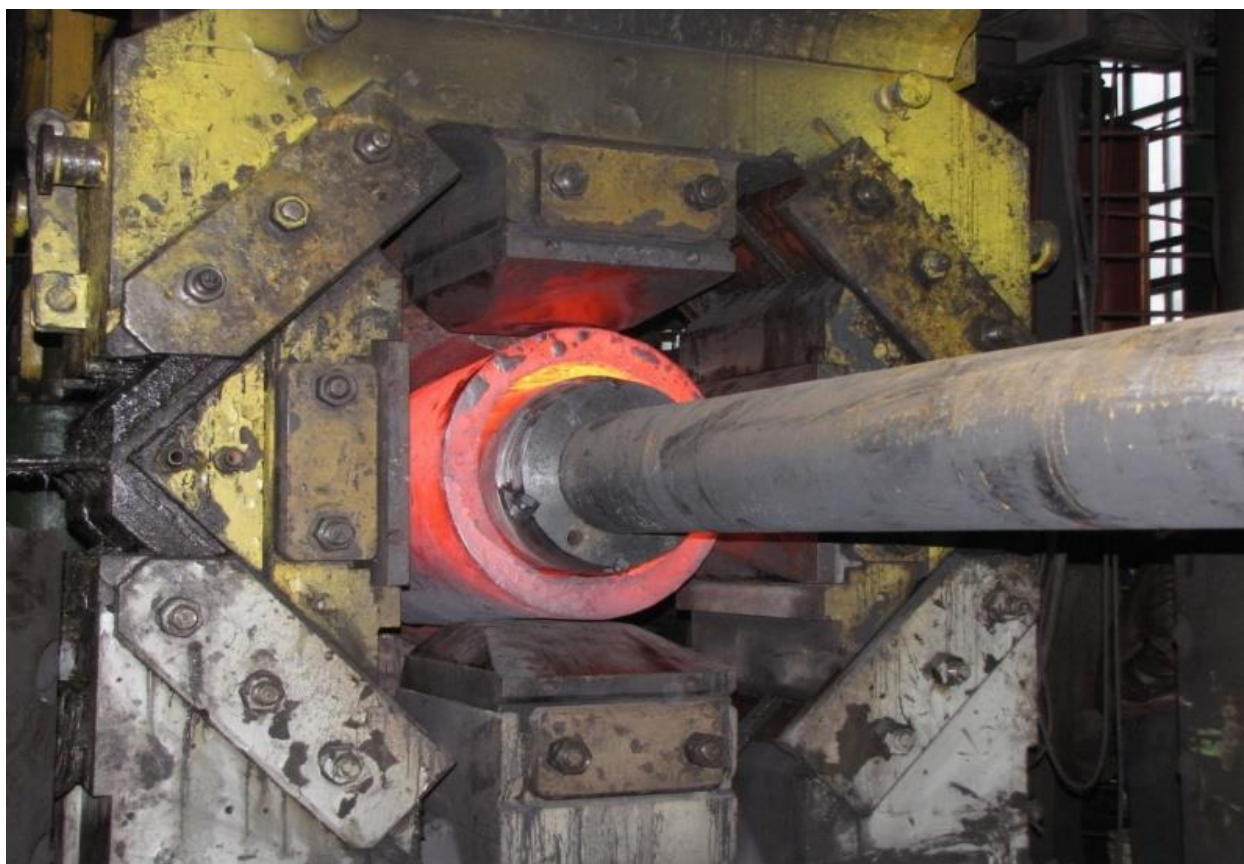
Ковка трубы на прессе в 4-х бойковом ковочном устройстве на короткой оправке
